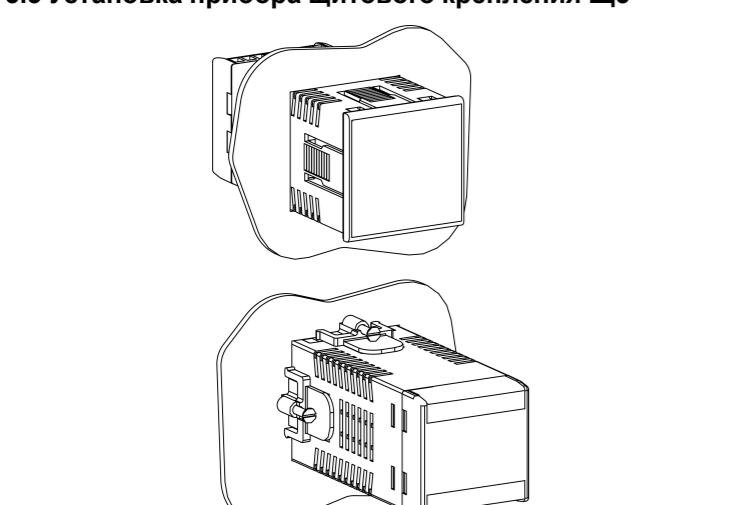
Монтаж прибора щитового крепления Щ5
